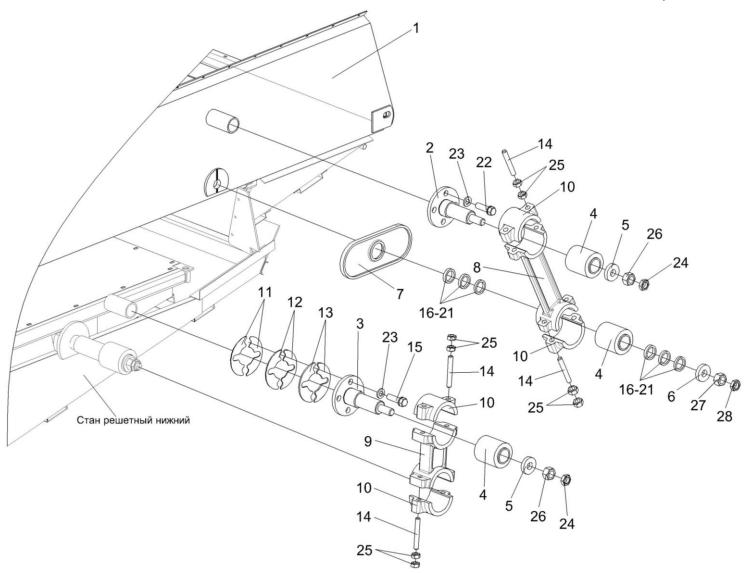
Установка привода стана решетного верхнего КЗК 0260000Б-01
